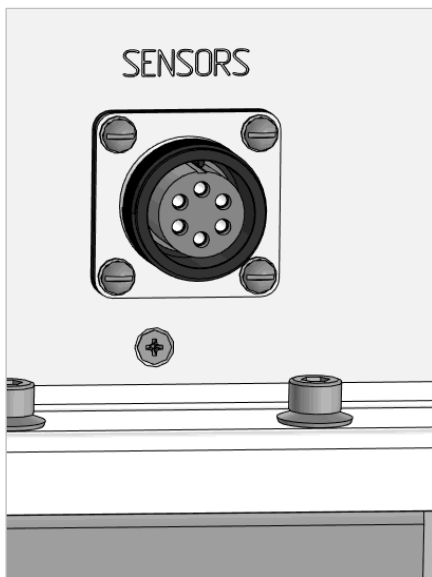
Соединитель «SENSORS» блоков FSC и FSR1
